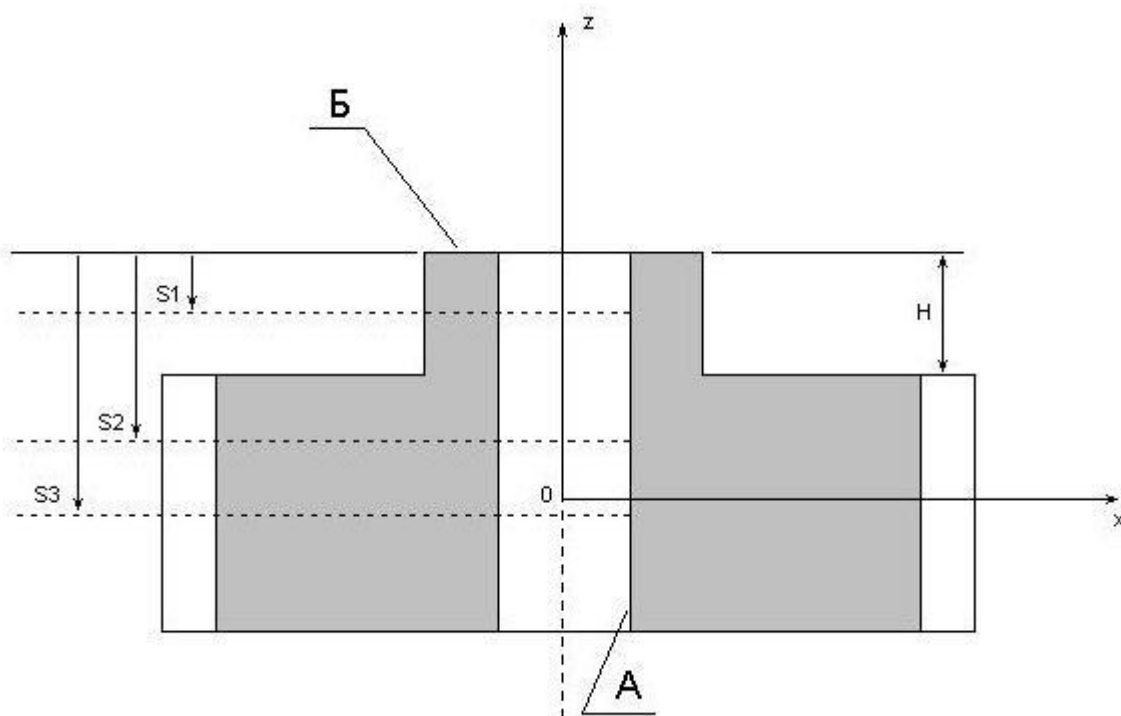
Расположение сечений базового цилиндра
